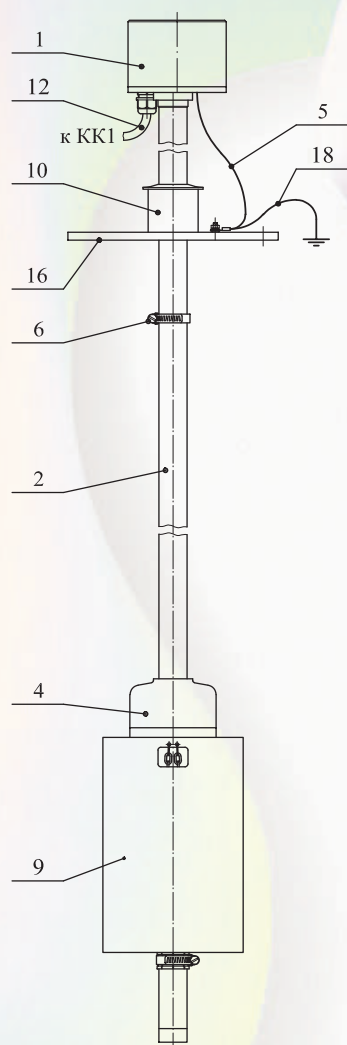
Эскиз доработки крышки резервуара для установки ППП1 (АПЖ) на двух фланцах
